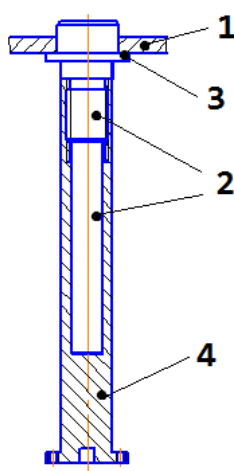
Схематический чертёж держателя образца. 1 – внутренняя стальная стенка сосуда Дьюара; 2 – сплошной медный стержень; 3 – соединение сваркой; 4 – основной подвижный держатель образца
